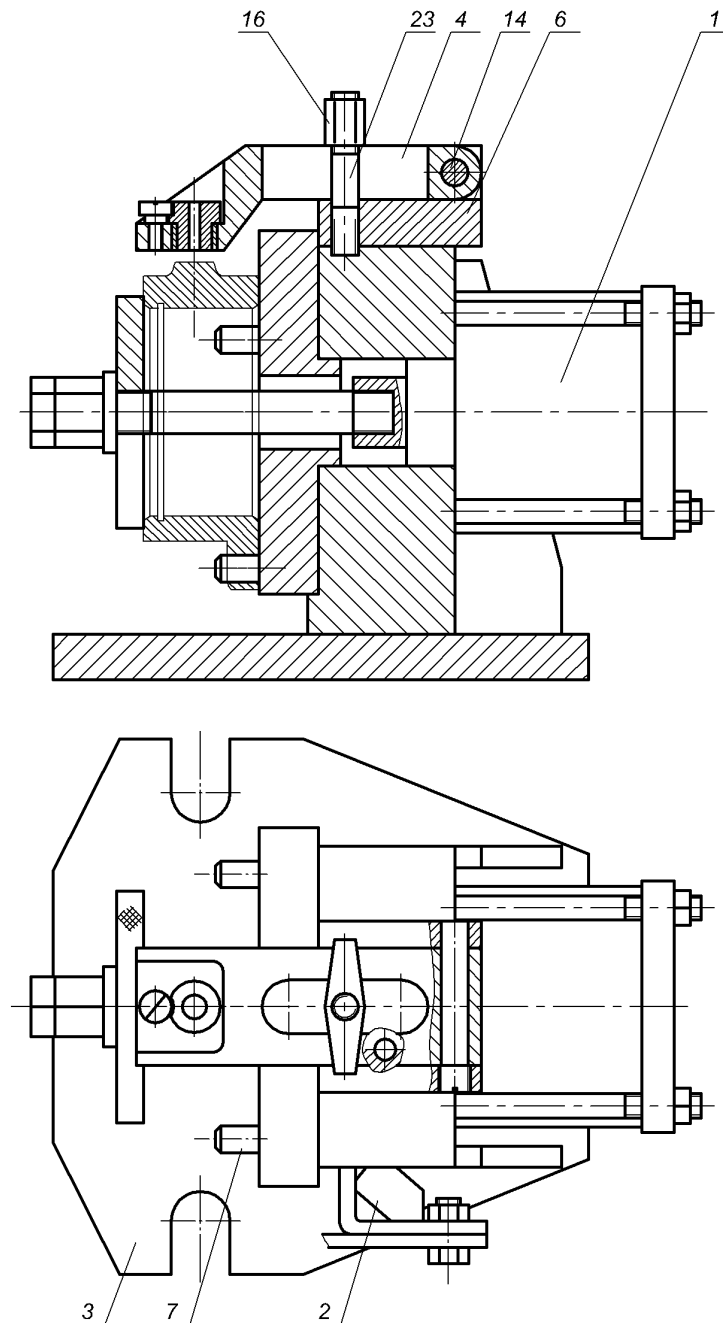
Кондуктор для свердління отв. $\varnothing 4$ мм, розсвердлювання і нарізання різі K1/8" у деталі «Корпус підшипника 21-2501В»
